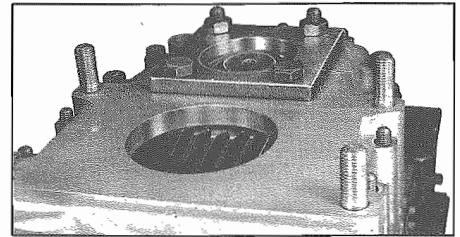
Controllo della posizione dell'albero secondario Checking the bearing of countershaft
